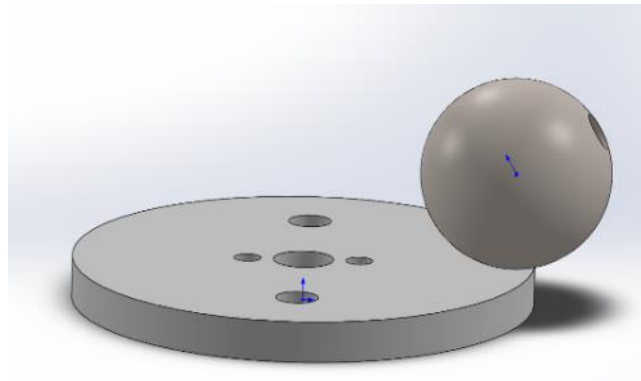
Ensamble del par tribológico diseñado en solidworks.
